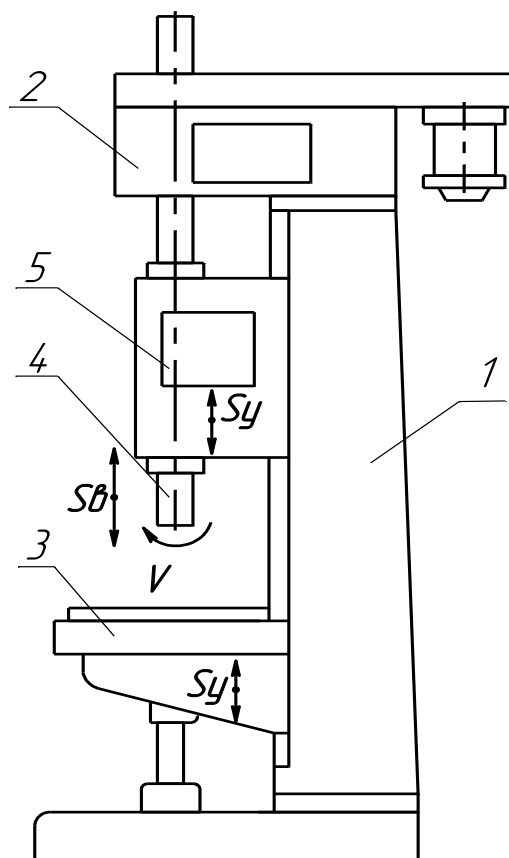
Загальний вигляд вертикально-свердлильного верстата
